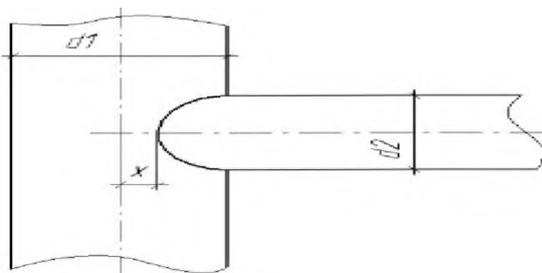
Схема Т-образного сварочного соединения
